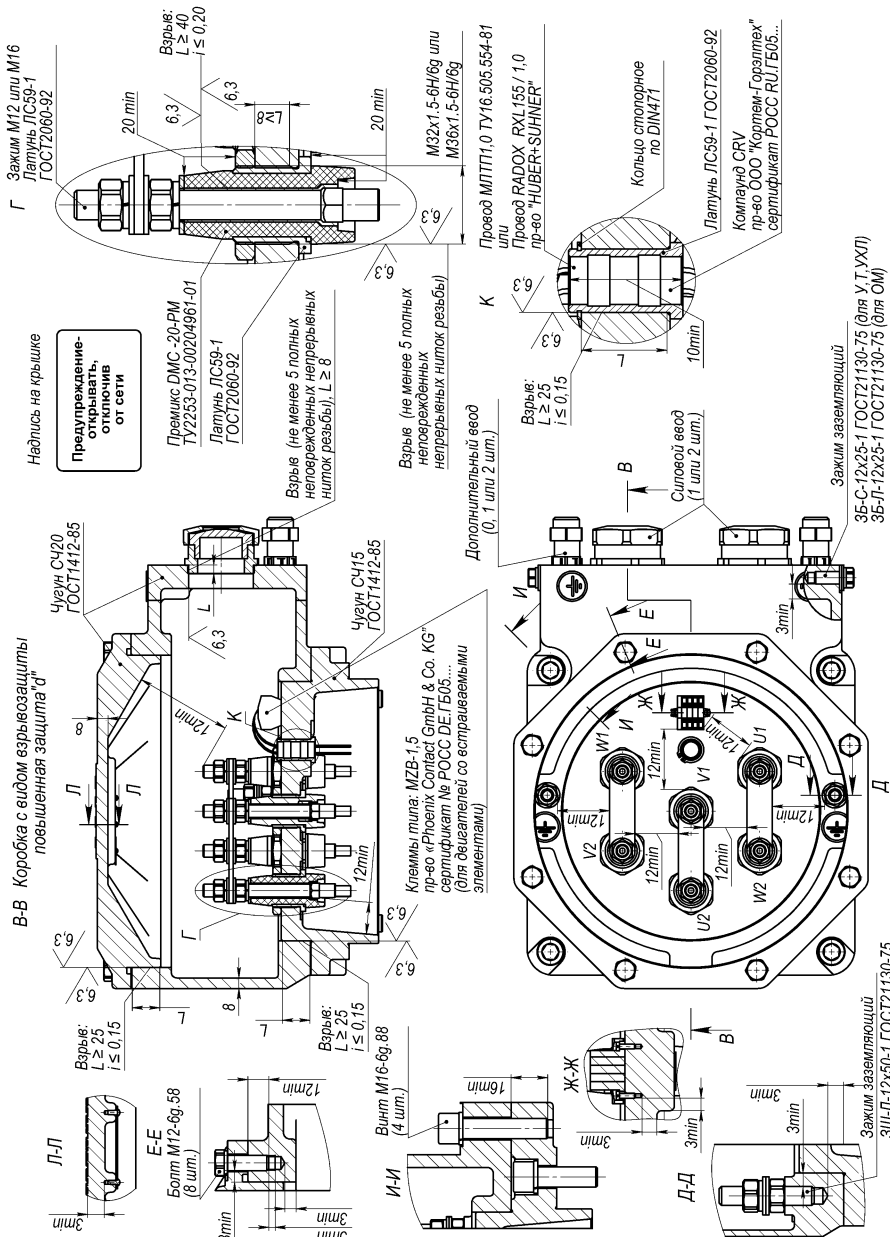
Чертеж взрывозащиты коробки выводов «d»
